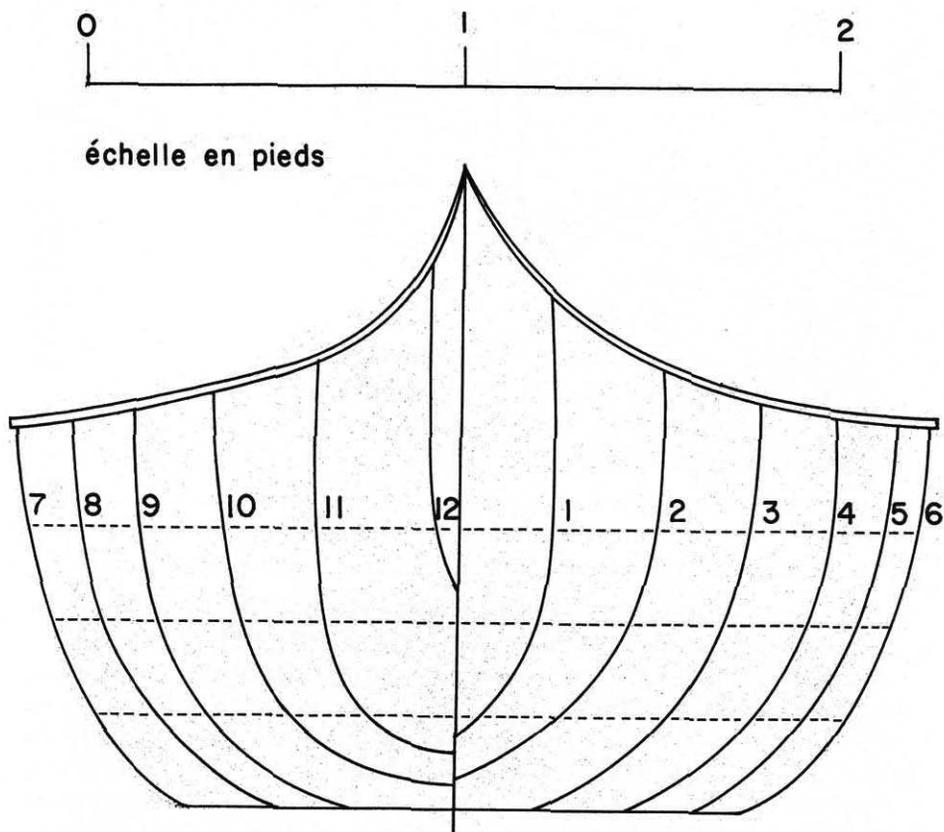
Plan du canot construit à Weymontaching (été 1966)
